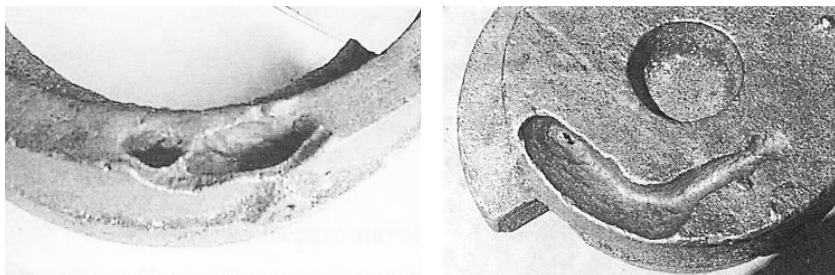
Виливки з газоусадочними раковинами:
